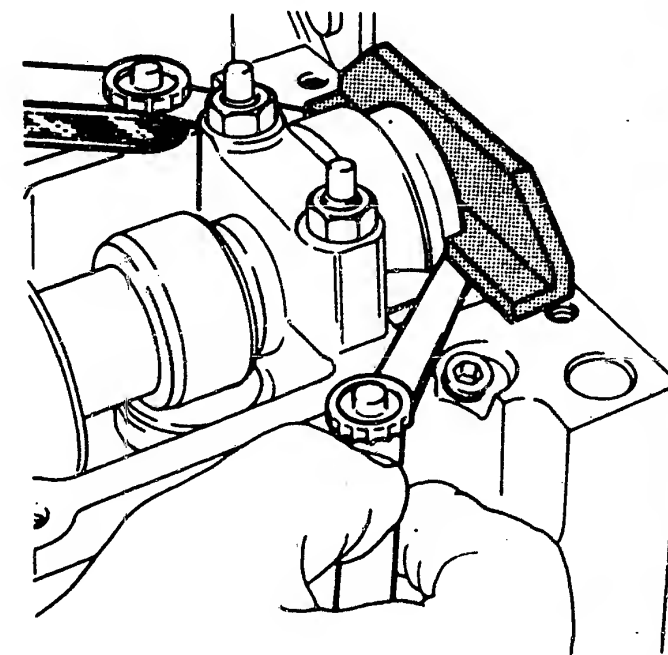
Diesel-Motor: Mit dem Winkelleisen und dem Unterlegen von gleich dicken Blattlehren auf beiden Seiten wird die Nockenwelle exakt auf OT gestellt.
